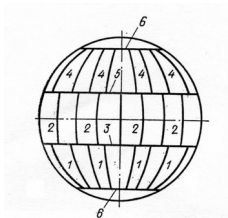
Схема ручной сварки сферического резервуара
